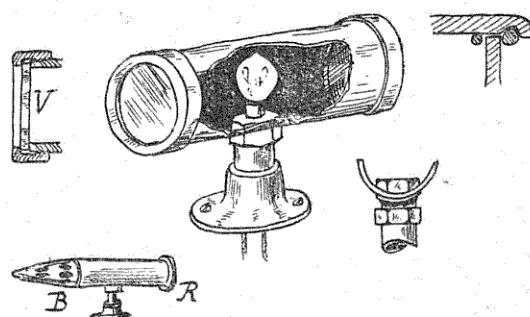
Lanterne à feu avant blanc B, à feu rouge R arrière.
